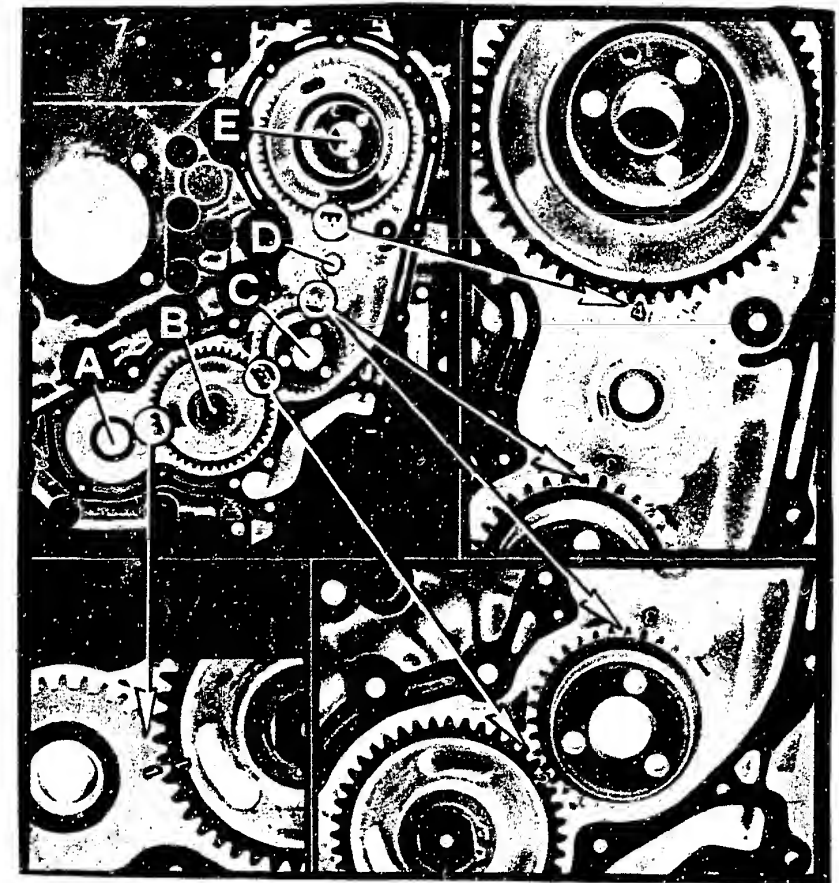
Motor 2500 turbo ds: Montieren und Einstellen der Steuerräder: A = Kurbelwelle, B = Zwischenrad, C = Antriebsrad der Unterdruckpumpe, D = Ölpumpenantrieb, E = Einspritzpumpenrad.
